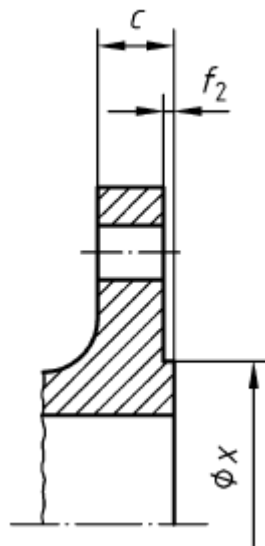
Esquema dimensional de cara elevada de brida plana tipo Pygot
